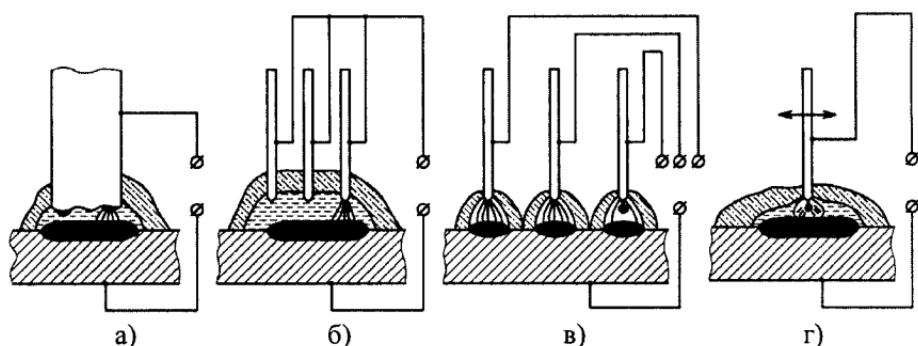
Різновиди наплавлювання під шаром флюсу
